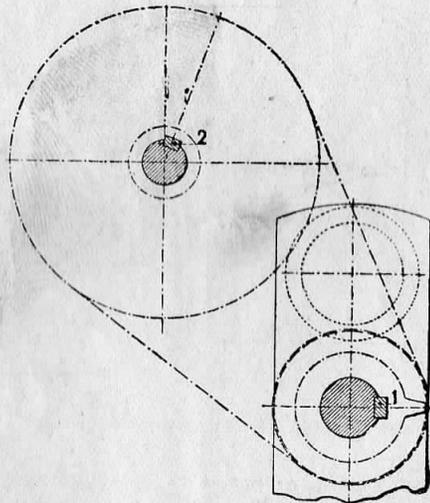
Position du pignon de vilebrequin et de la roue d'arbre à excentriques lorsque le piston du premier cylindre est au point mort haut de compression.
